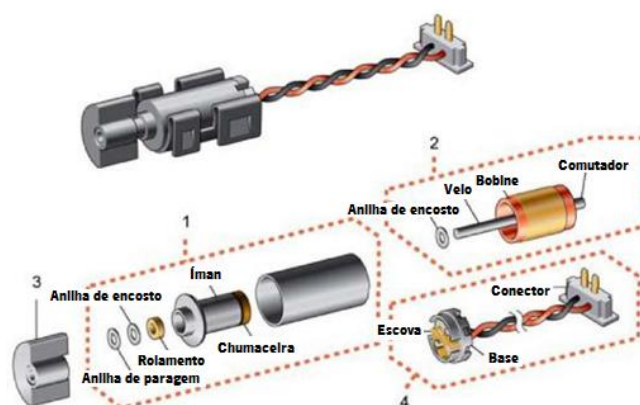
Construção do motor DC que produz vibração, com configuração cilíndrica: 1 montagem do estator; 2 montagem do rotor; 3 excêntrico e 4 montagem das escovas (adaptada de [21]).
